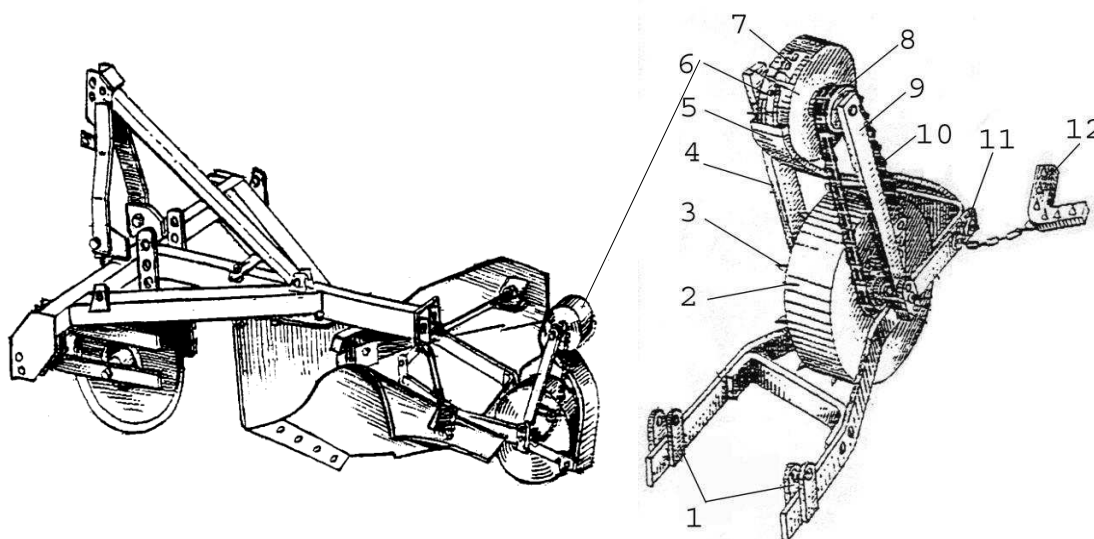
Плуг ПКЛ-70 с высевальным приспособлением: 1 – кронштейны крепления к корпусу плуга; 2 – опорно-приводной каток; 3 – грунтозацеп; 4, 9 – левая и правая траверсы; 5 – направляющий лоток; 6 – семенной барабан; 7 – лючок; 8 – звездочка; 10 – цепь привода; 11 – башмак; 12 – гребенка
